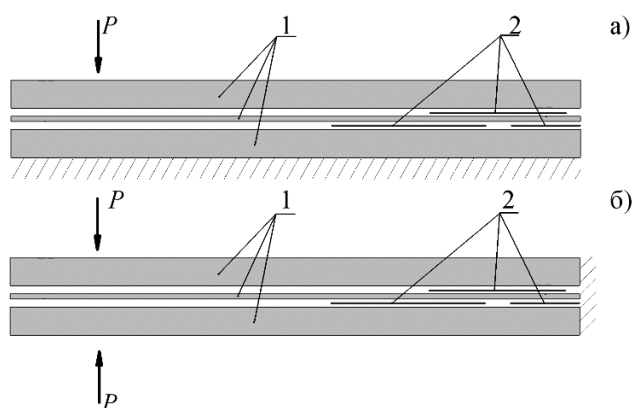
Схема расположения листовых заготовок и ПСП. Цифрами обозначены: 1 - листовые заготовки, 2 – ПСП.
